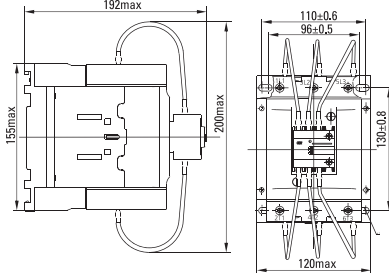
Габаритные и установочные размеры контакторов 110квар
